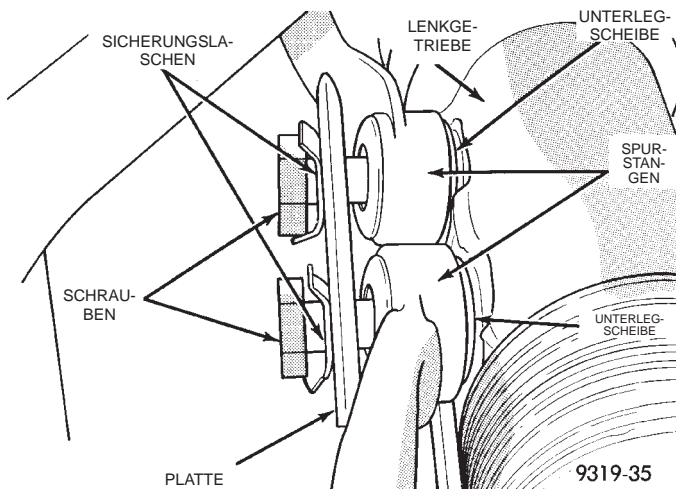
Befestigung der Spurstangen am Lenkgetriebe
